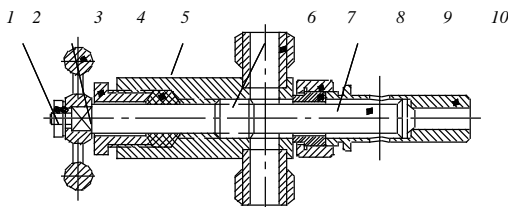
Приспособление КИ-6272: 1 – гайка; 2 – шайба; 3 – маховичок; 4 – гайка нажимная; 5 – набивка; 6 – штуцер; 7 – гайка накидная; 8 – ниппель; 9 – игла запорная; 10 – штуцер переходной
